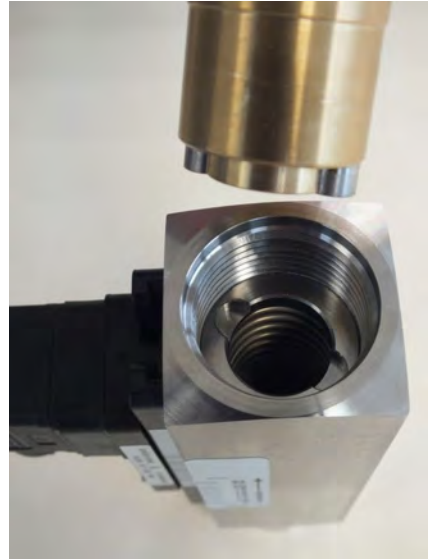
Eindrehwerkzeug-Gewindering einführen (Ausgang)
